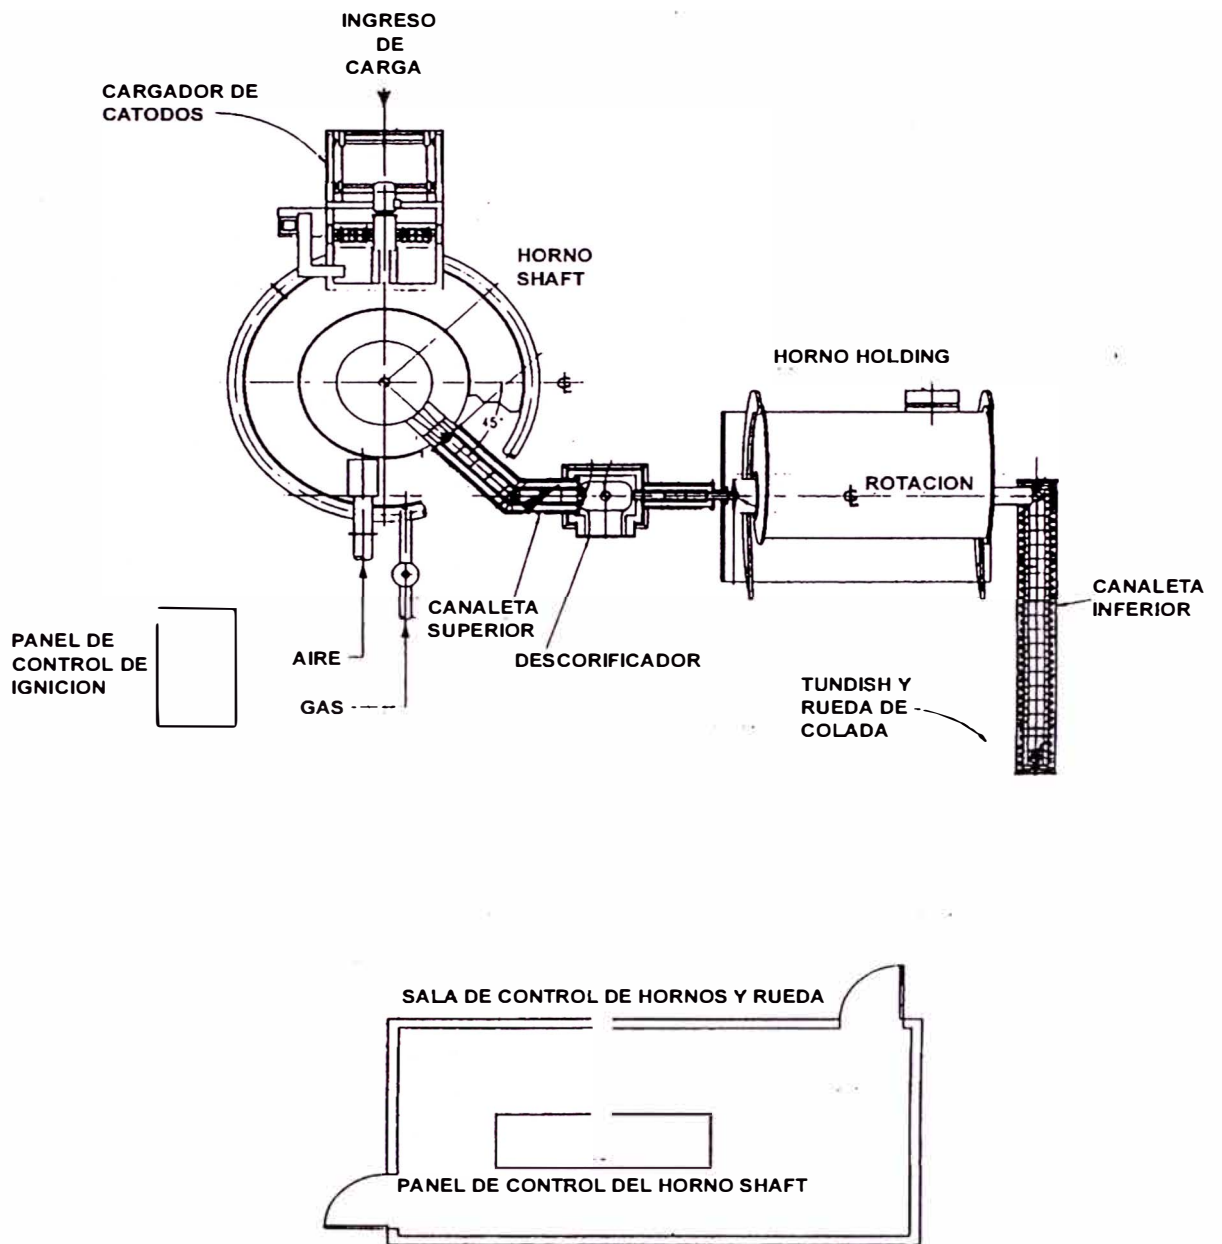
Hornos Shaft y Holding (vista de planta)
